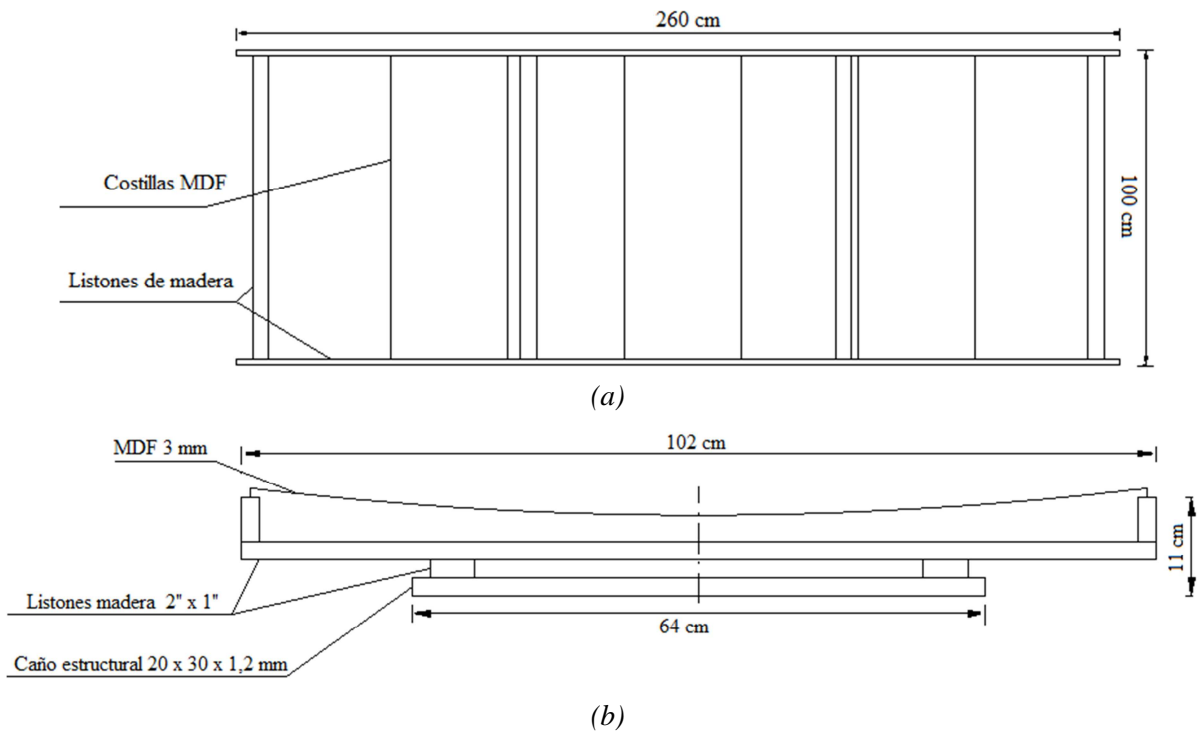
vistas de planta (a) y corte (b) de la estructura del reflector
